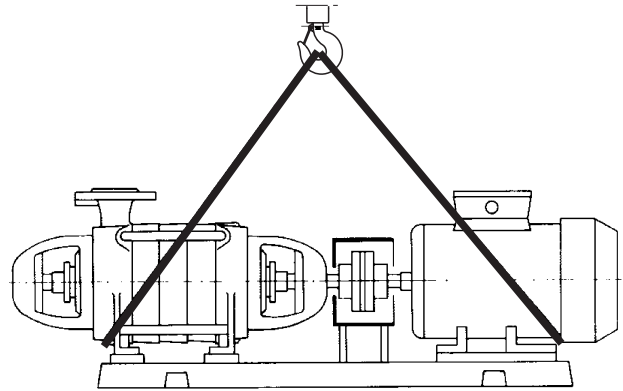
Hebezeug befestigen an horizontalem Pumpenaggregat
